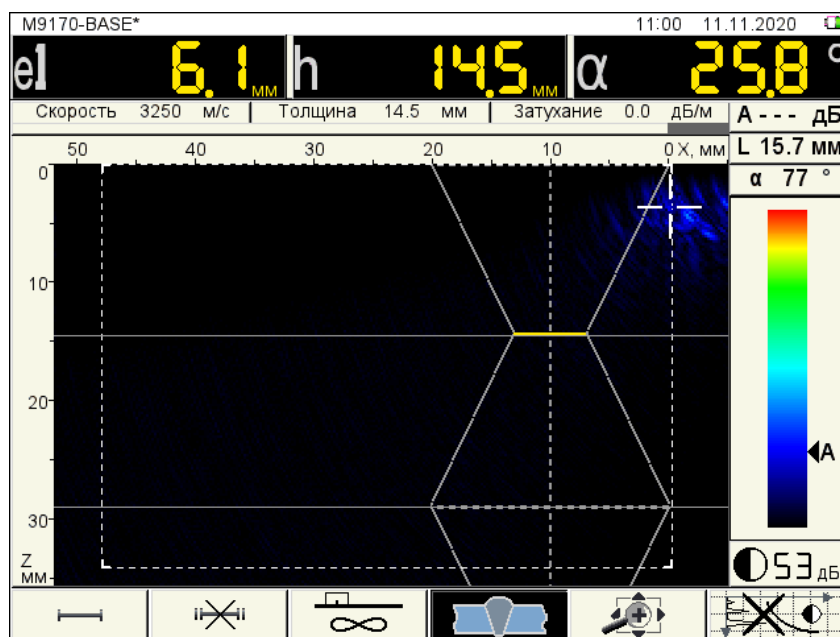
Установка масштаба, первого строга и маски сварного шва
